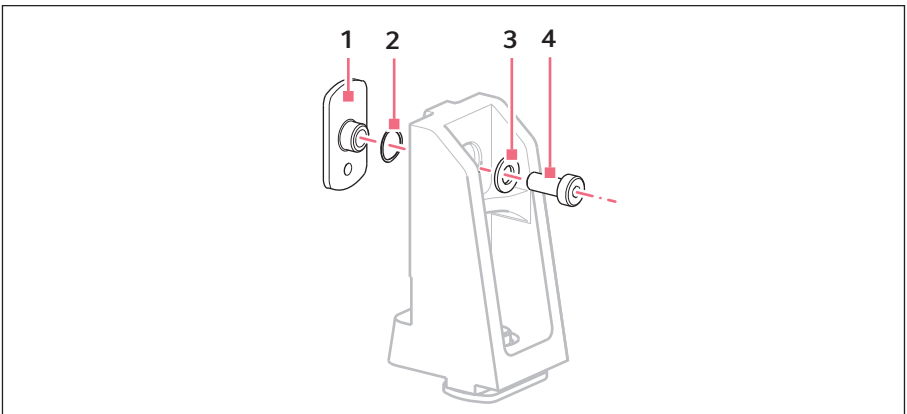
Cosse – position des disques à l'exemple du porte-module Z
